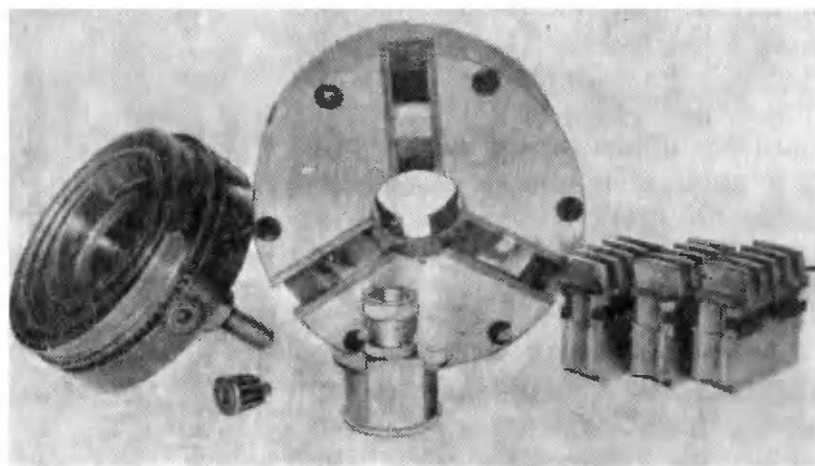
Основные части механизированного патрона станка типа АТПр-2М12У.
